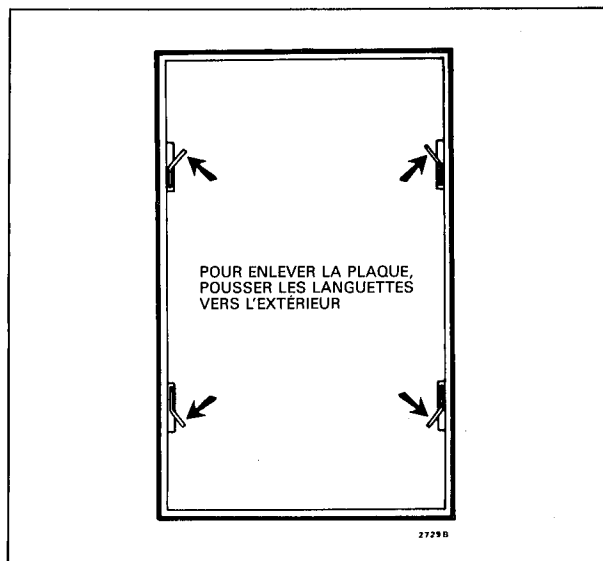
CHANGEMENT DE LA PLAQUE DE RECouvreMENT POUR UN MONTAGE HORIZONTAL.
